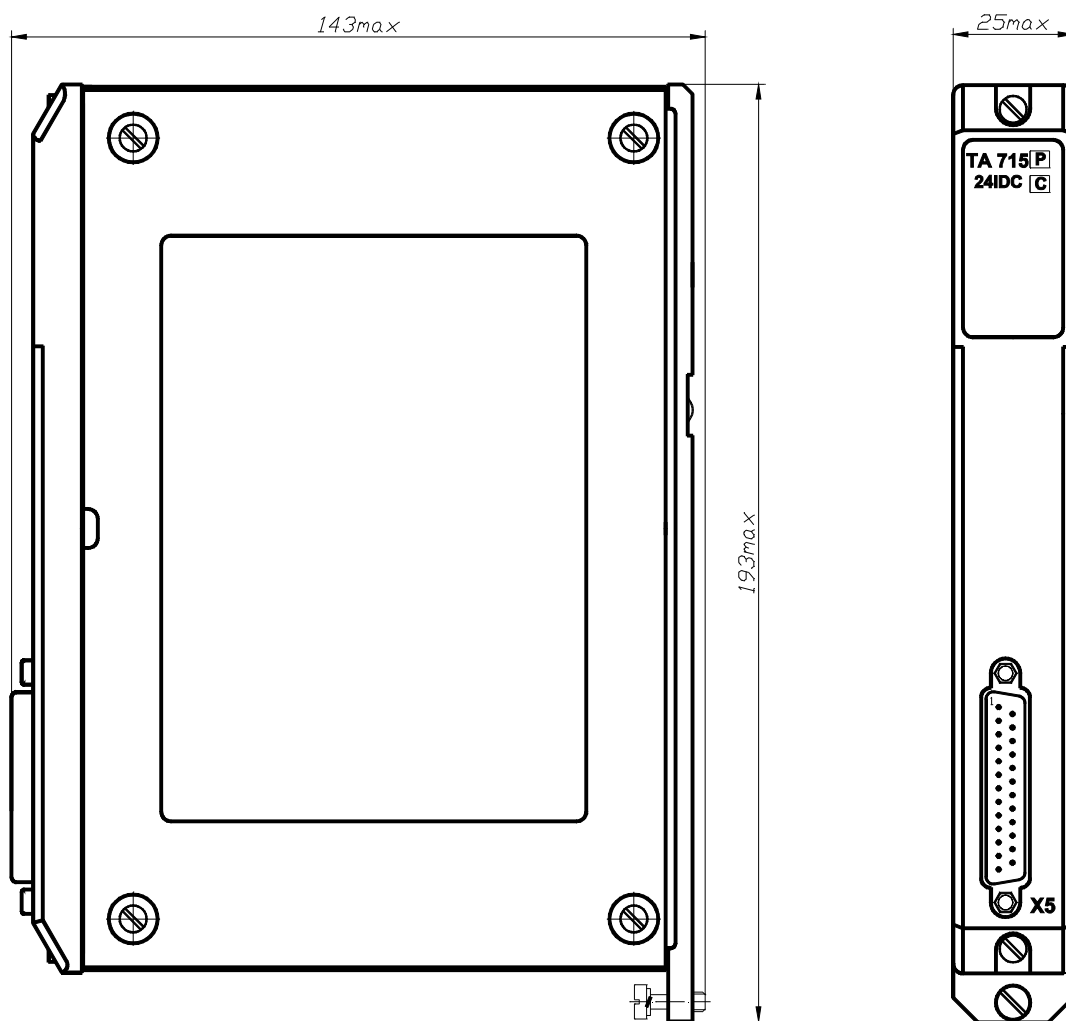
Модуль TA 715. Внешний вид и габаритные размеры
